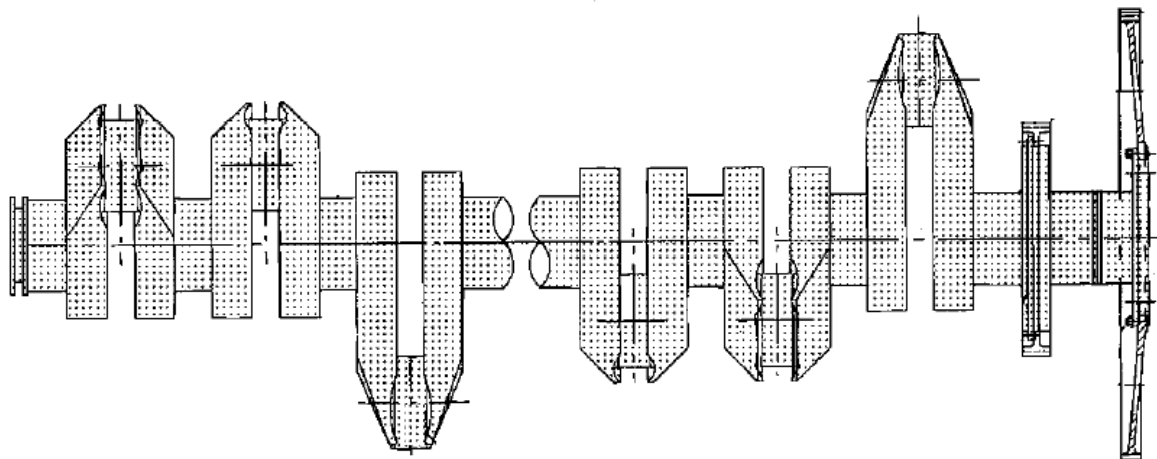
Колінчастий вал двигуна 6ДКРН 80/230
